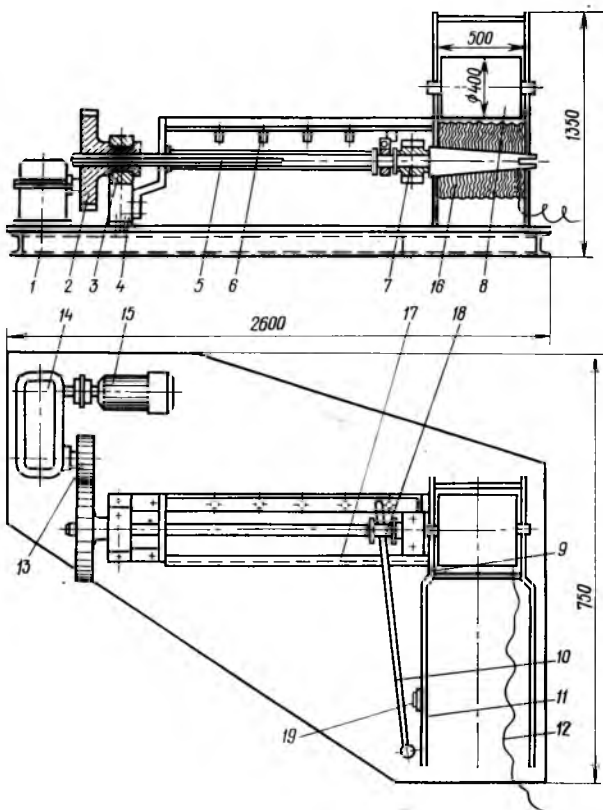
Машина для намотки использованной упаковочной проволоки в бухту:
